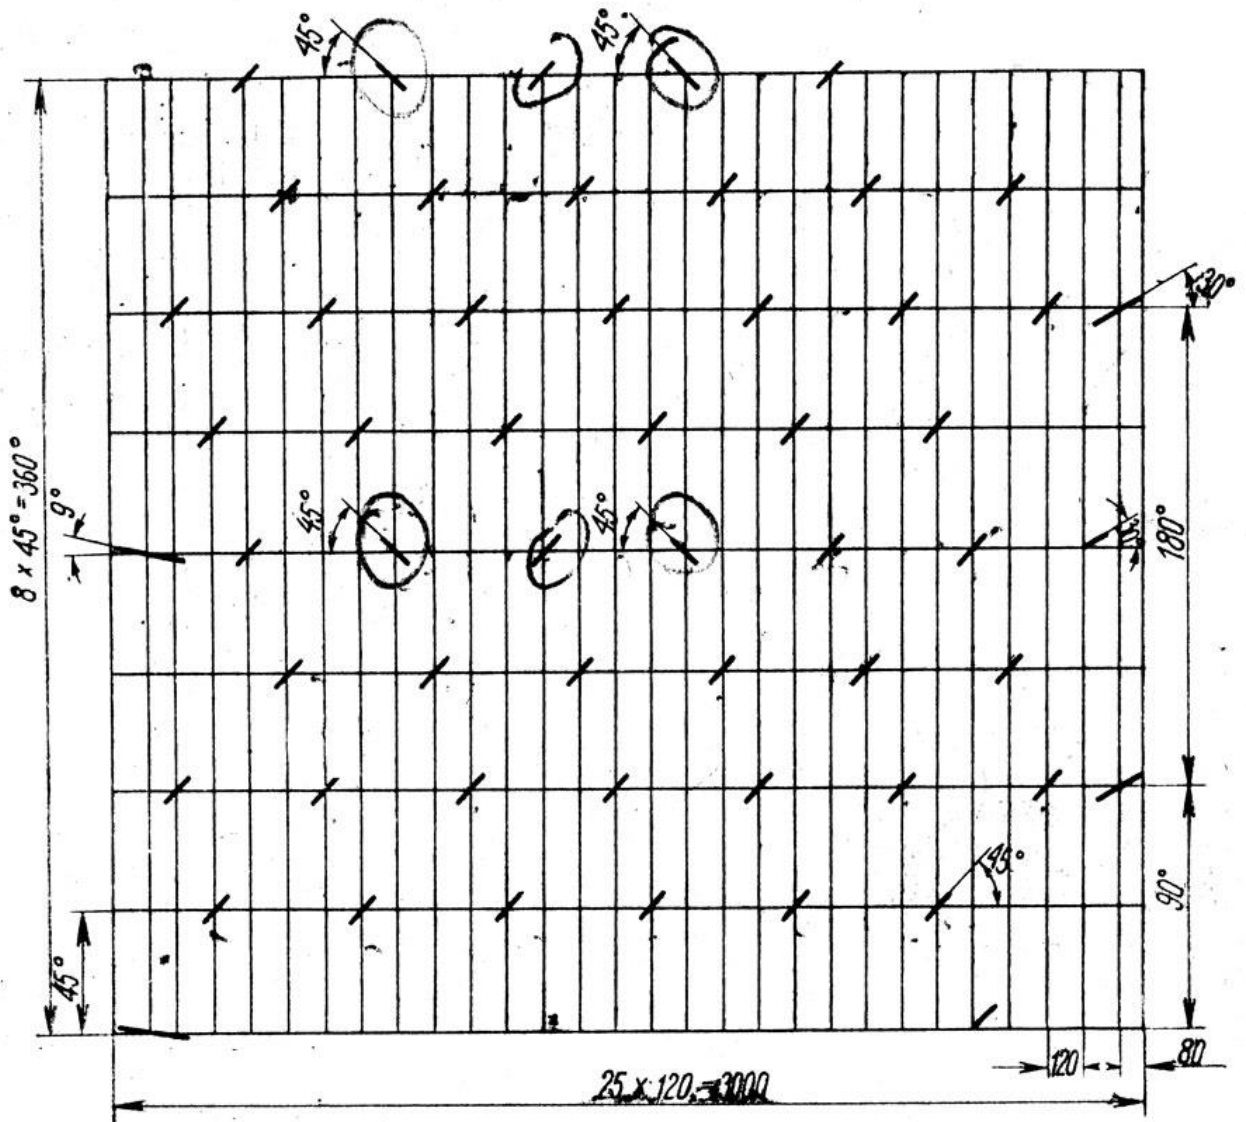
Схема расположения лопаток в сушилках непрерывного действия
